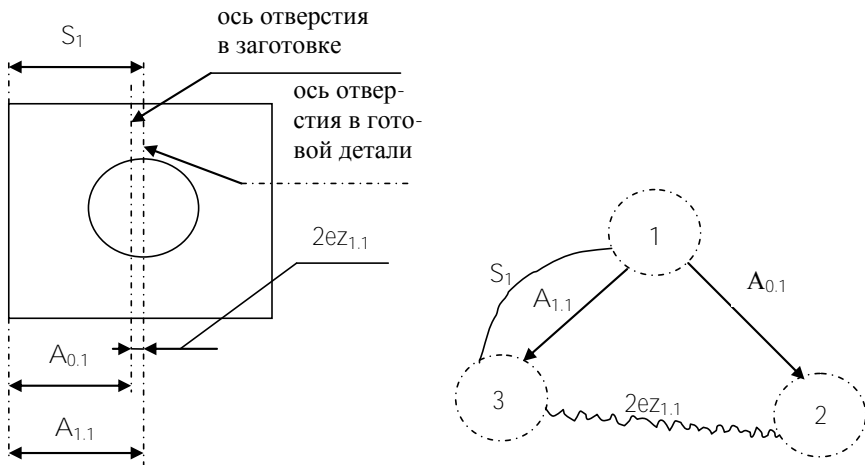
Схема обработки и граф размерных связей для детали с отверстием
